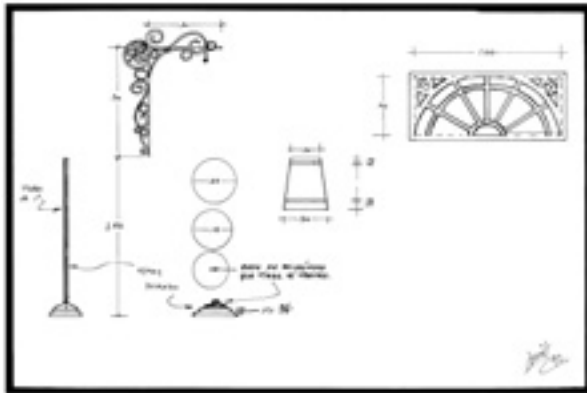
Lámpara de pie; se muestra detalles de cómo construirla.
